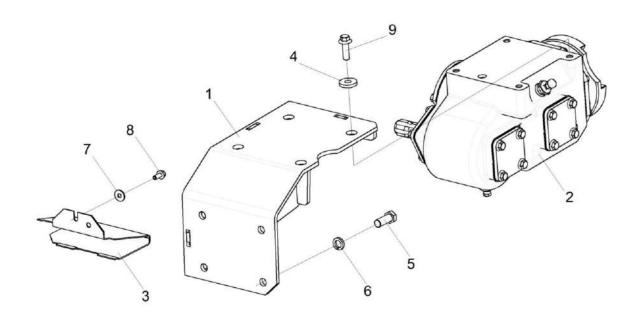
Установка привода жатки ЖКС-45-0100160
